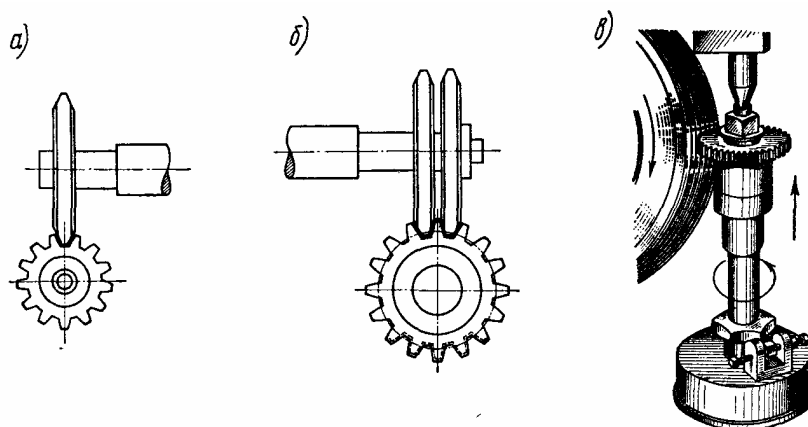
Зубошлифование цилиндрического зубчатого колеса:
